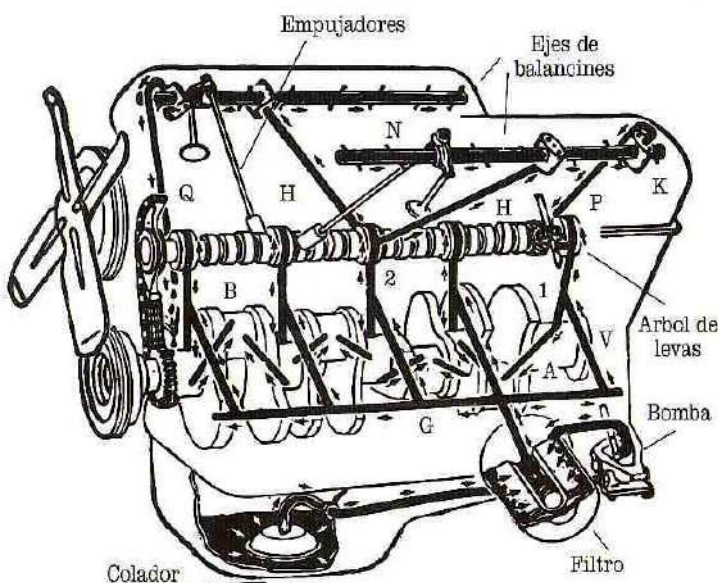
Engrase a presión en un motor OHV de 8 cilindros en V con eje de balancines.
